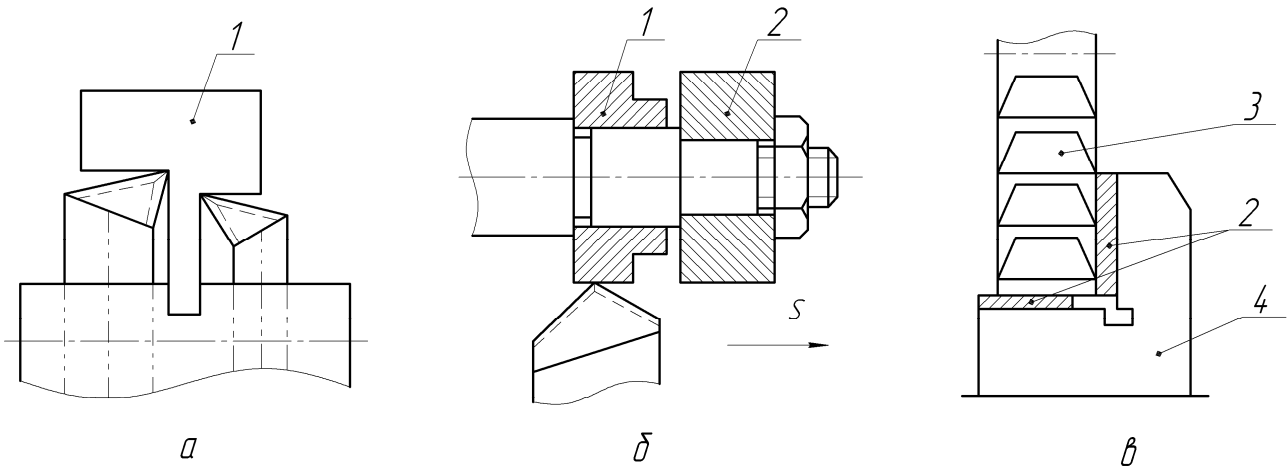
Схема й розрізи шаблонів для токарних і фрезерних верстатів: *а* – для встановлення двох різців на токарному верстаті (1 – шаблон); *б* – для встановлення різця на токарному верстаті (1 – настановне кільце; 2 – оброблювана деталь); *в* – для налаштування руху фрези у двох напрямках (1 – косинець; 2 – шаблон; 3 – фреза)
